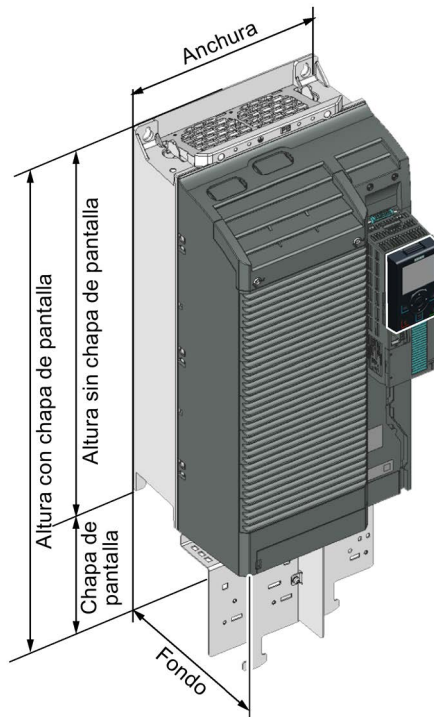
Dimensiones de PM240-2, FSA-FSG
